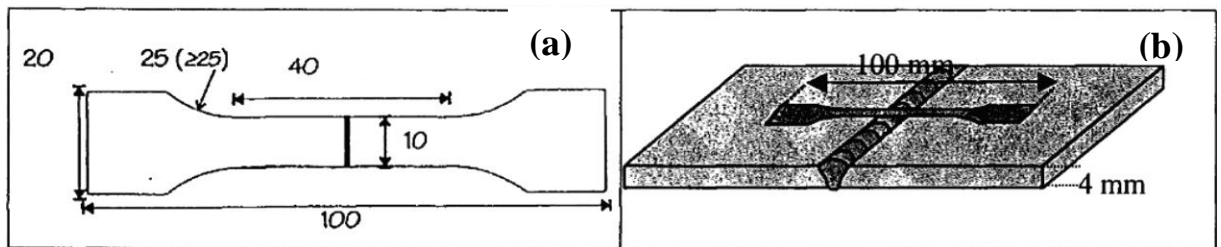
Eprouvettes de traction (a) Dimensions des éprouvettes, (b) Sens de prélèvement des éprouvettes.
